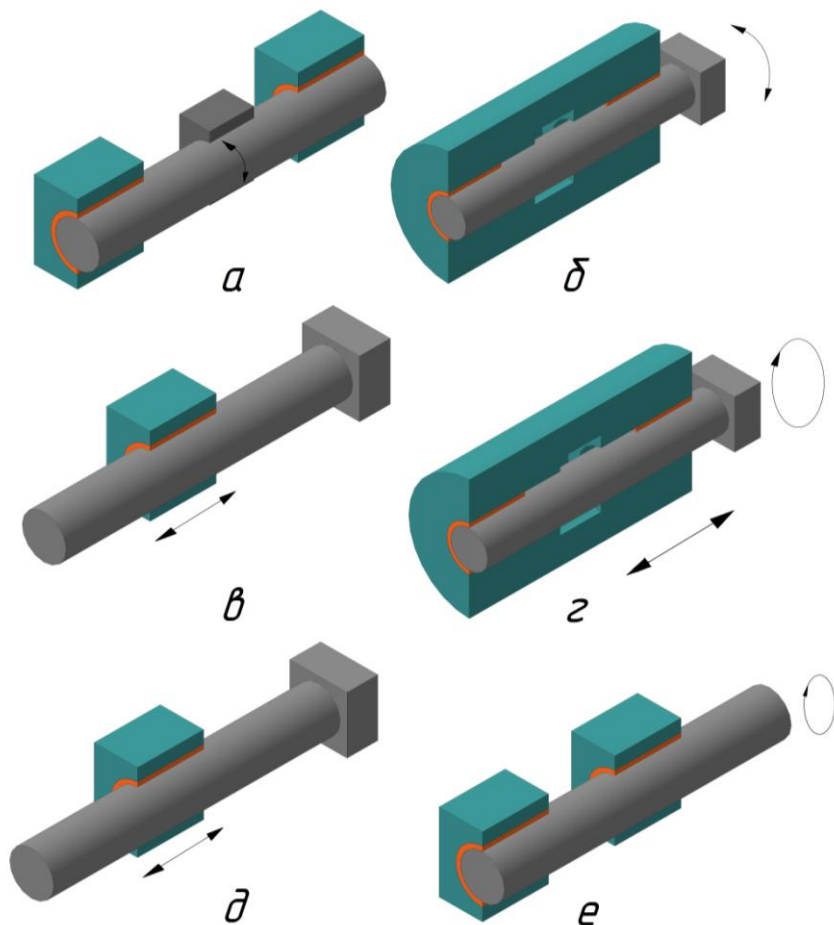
Конструктивные схемы подвижных сопряжений: а, б – шарниры; в, с, д – направляющие; е – подшипники скольжения
